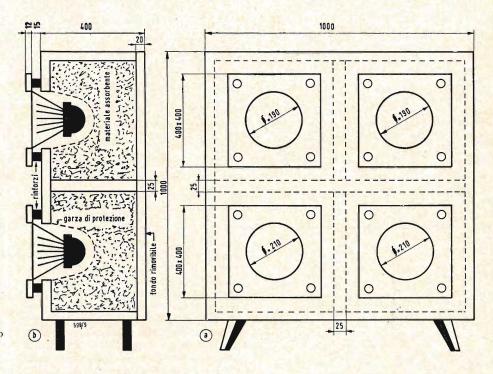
Dimensioni generali del mobile acustico (a) visto di fronte (b) visto di profilo.
